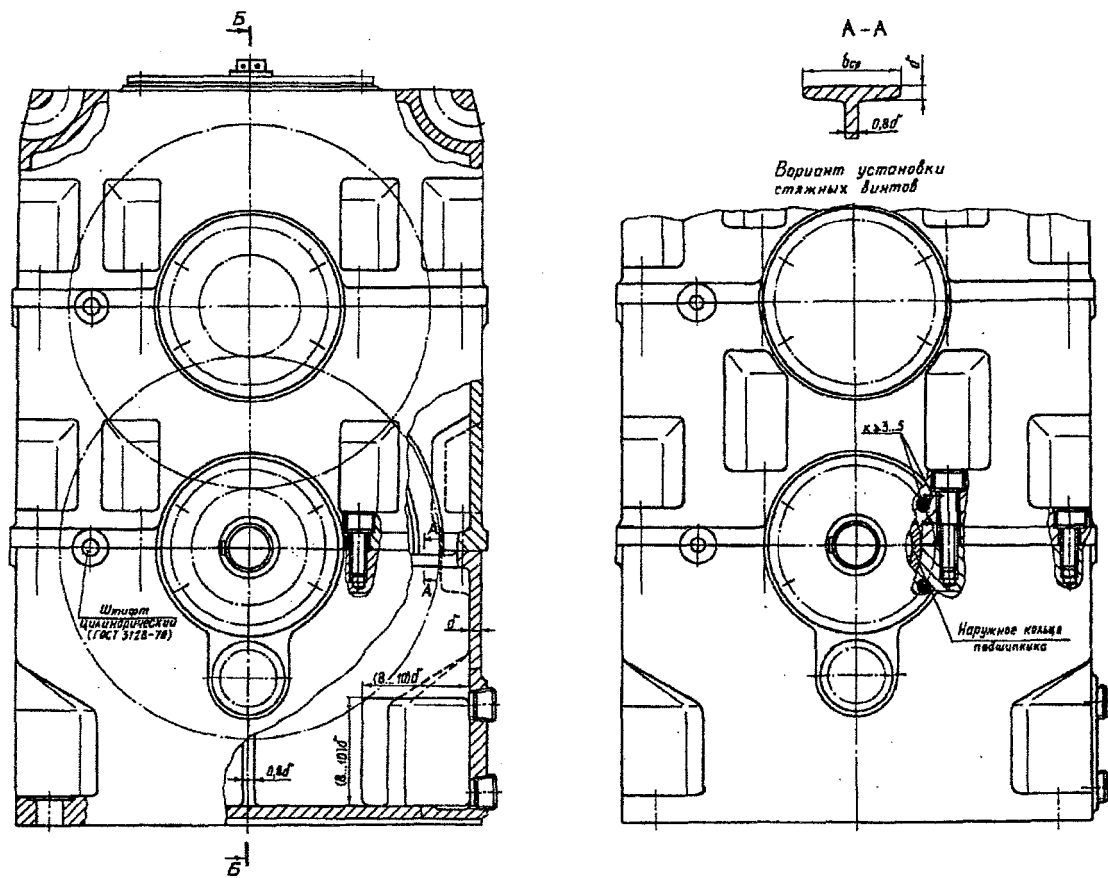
Двухступенчатый цилиндрический соосный редуктор с валами, расположенными в вертикальной плоскости
